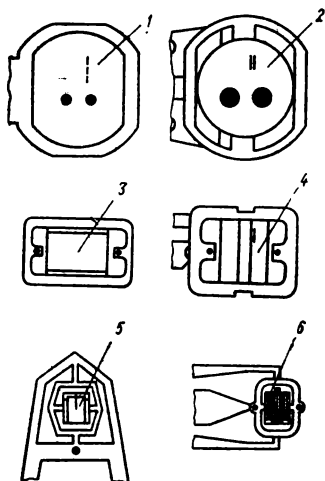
Конструкции опоры скольжения плавающей магнитной головки
